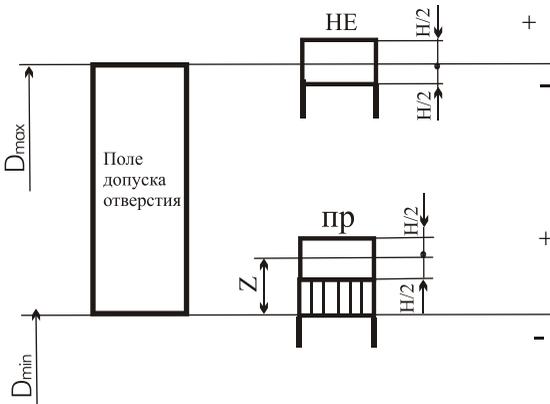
Схемы расположения полей допусков калибров
